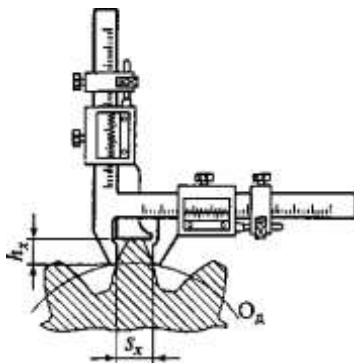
Измерение толщины зуба колеса цилиндрической передачи:
